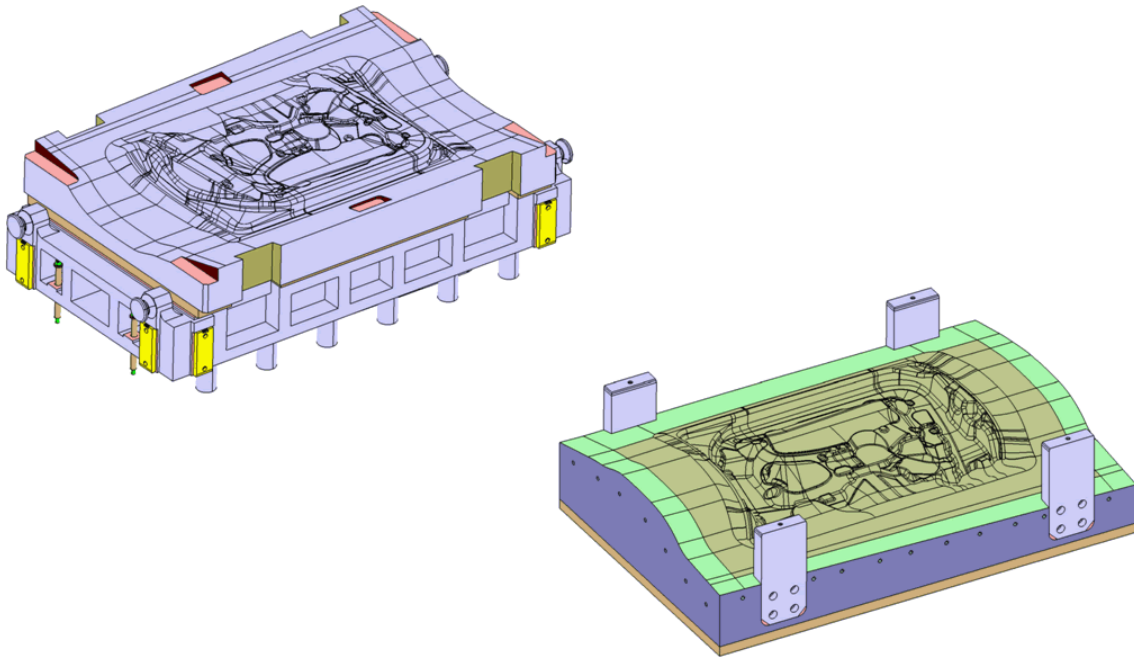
prinzipieller Werkzeugaufbau Innenteil
